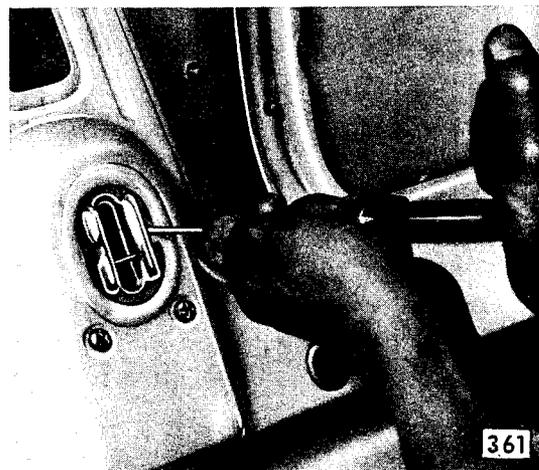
Haltelappen des Montageloch-Verschlußdeckels aufbiegen
